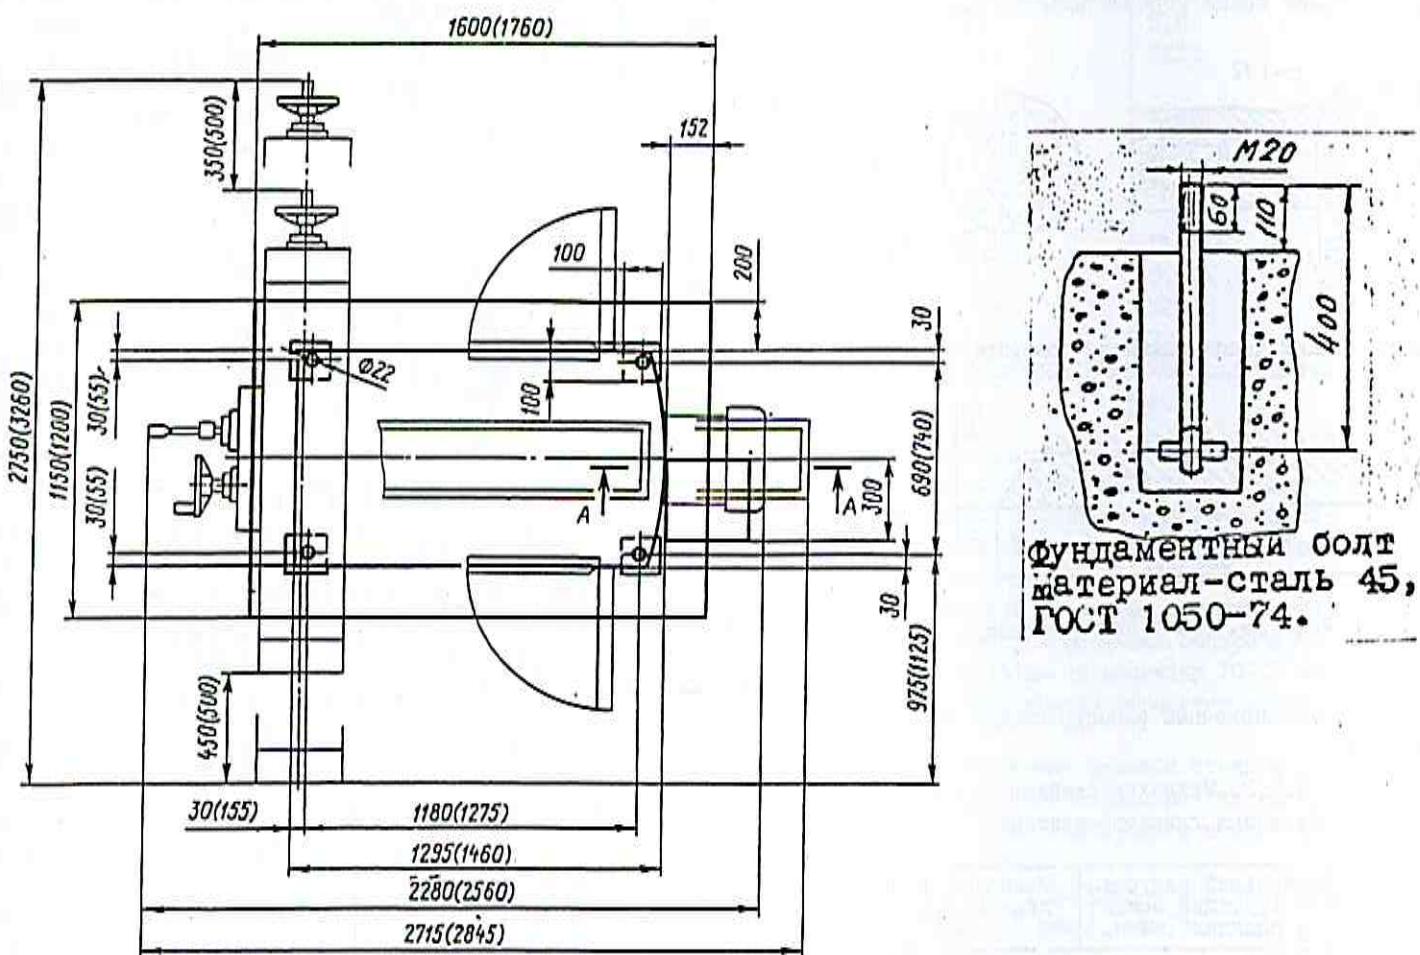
Установочный чертеж станков (размеры в скобках приведены для станка 6Р83Ш)
